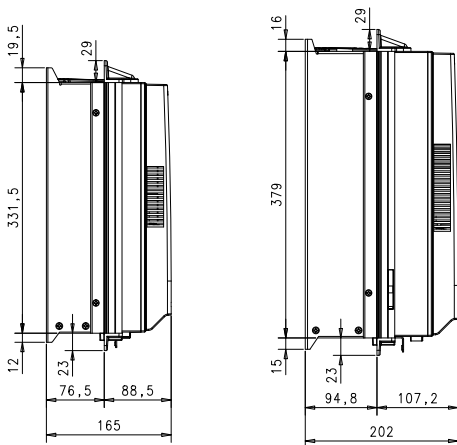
Dimensões da profundidade para montagem com flange do MR4 e MR5 (unidade: mm)
